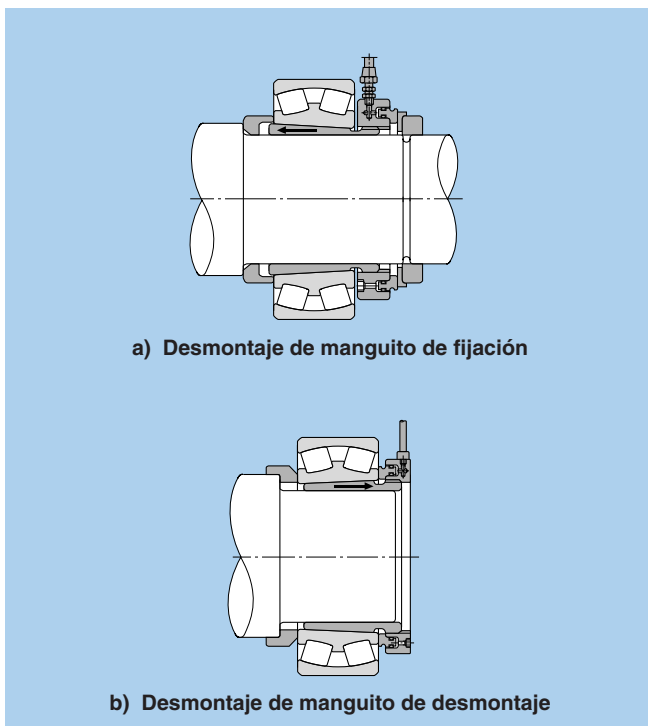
Desmontaje de rodamiento con manguito de desmontaje
